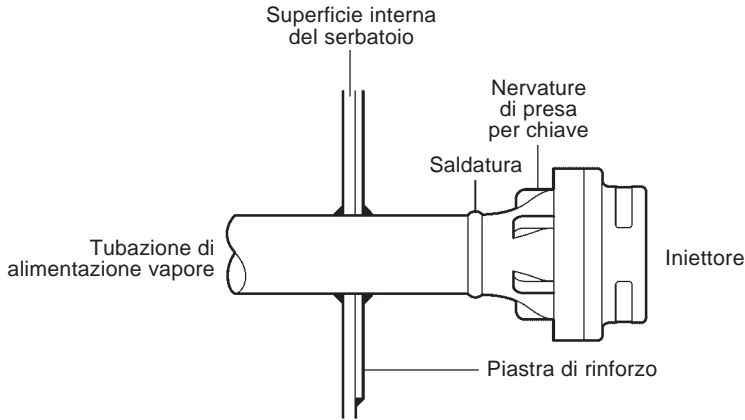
Iniettori IN25M e IN40M a saldare di testa - Tipica installazione con montaggio supportato dalla tubazione di alimentazione fissata a parete del serbatoio
